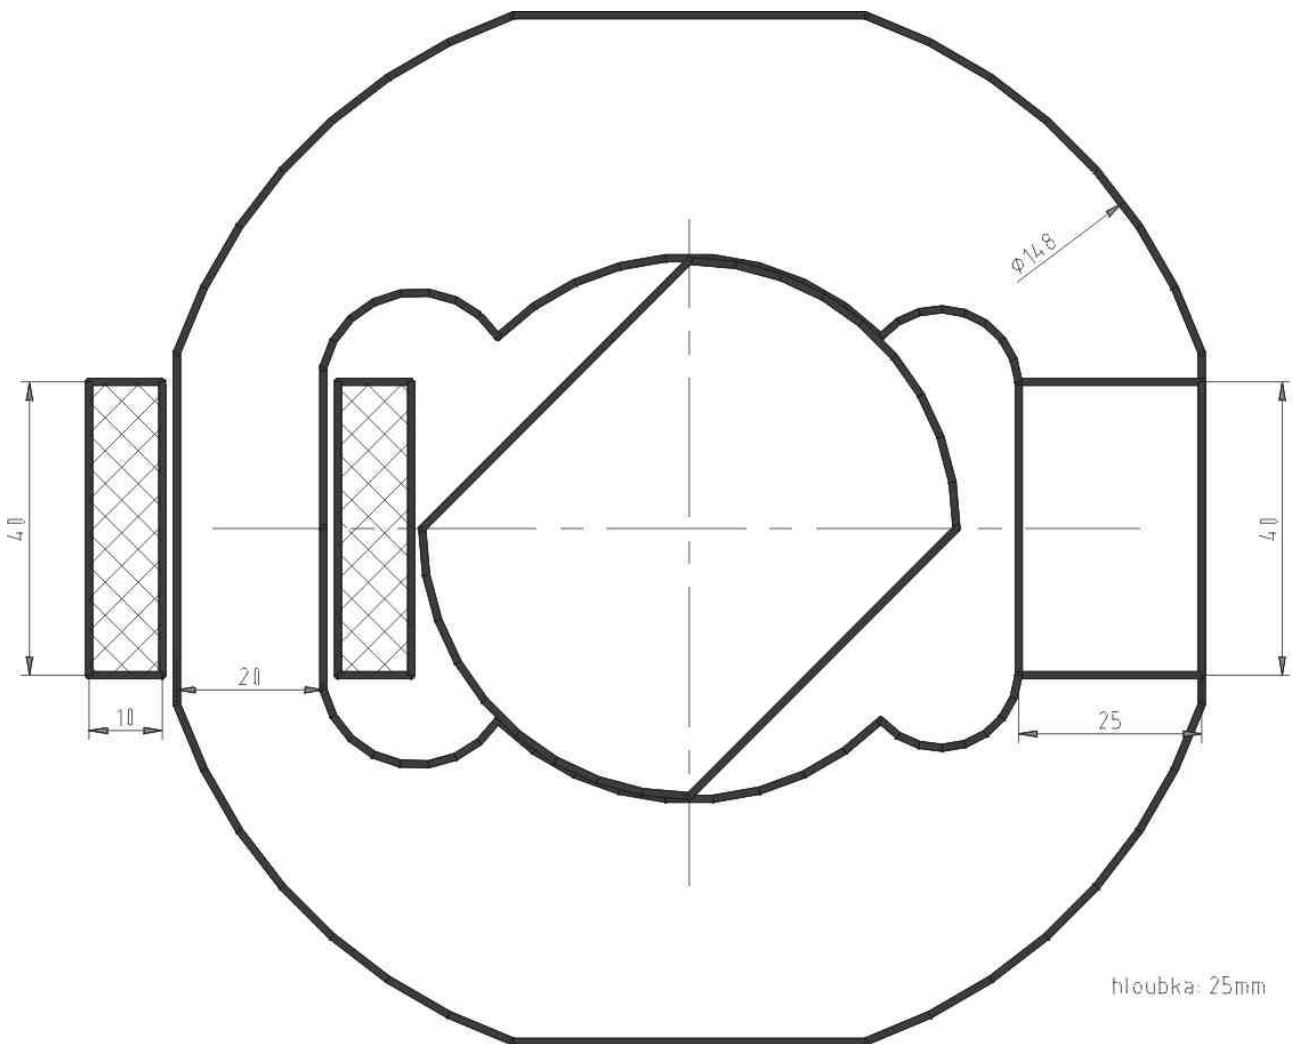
Konstrukční provedení jednofázového motoru 4-4.
